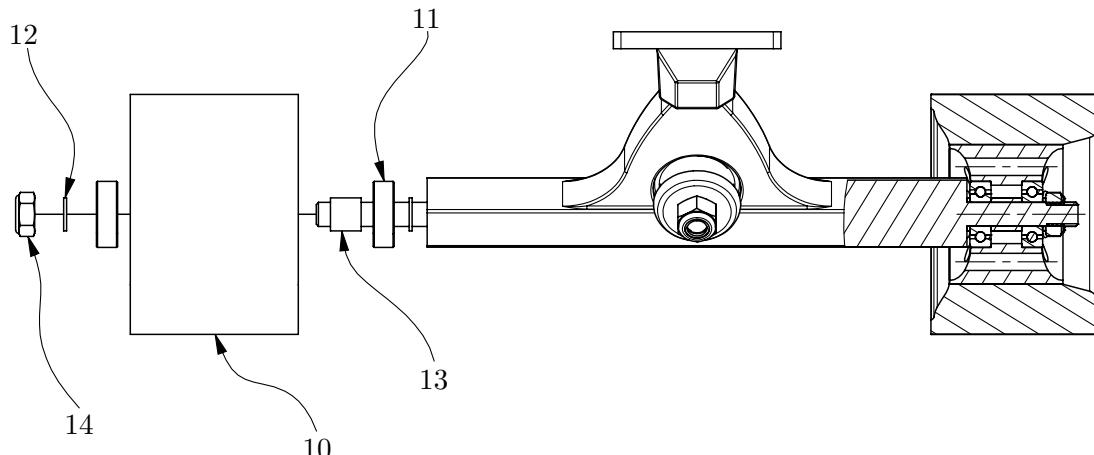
Aufbau eines der Trucks als Explosionsansicht exemplarisch an einem CALIPER II. Sichtbar sind hier:
